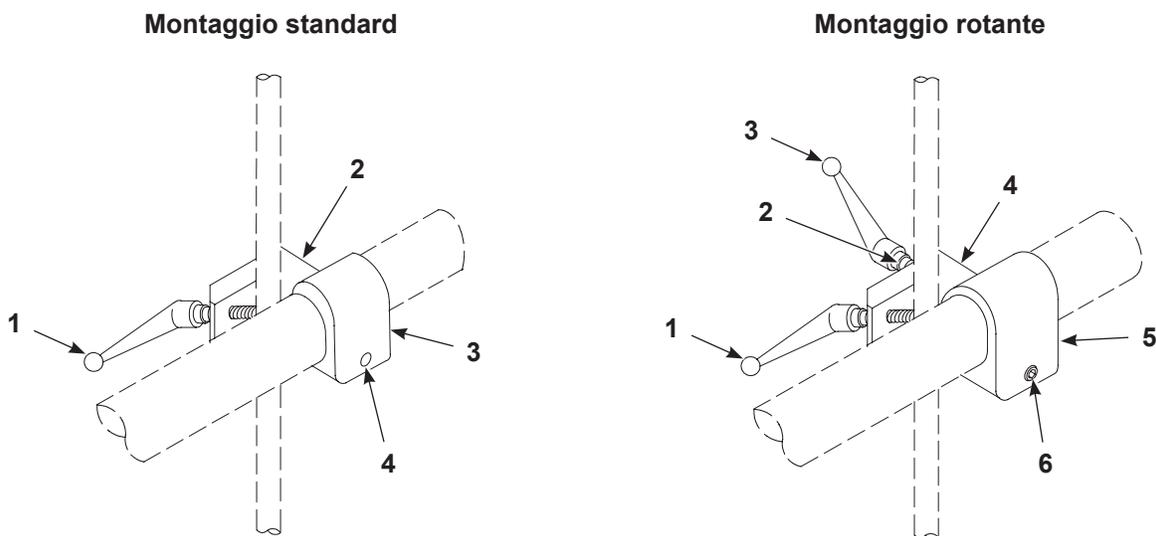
Elementi di montaggio su barra per pistole a spruzzo con montaggio su tubo
